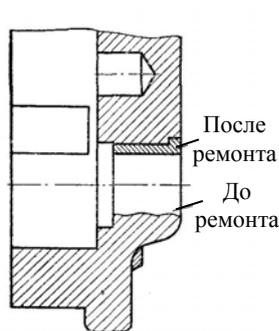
Схема установки втулки подшипника в изношенном корпусе
